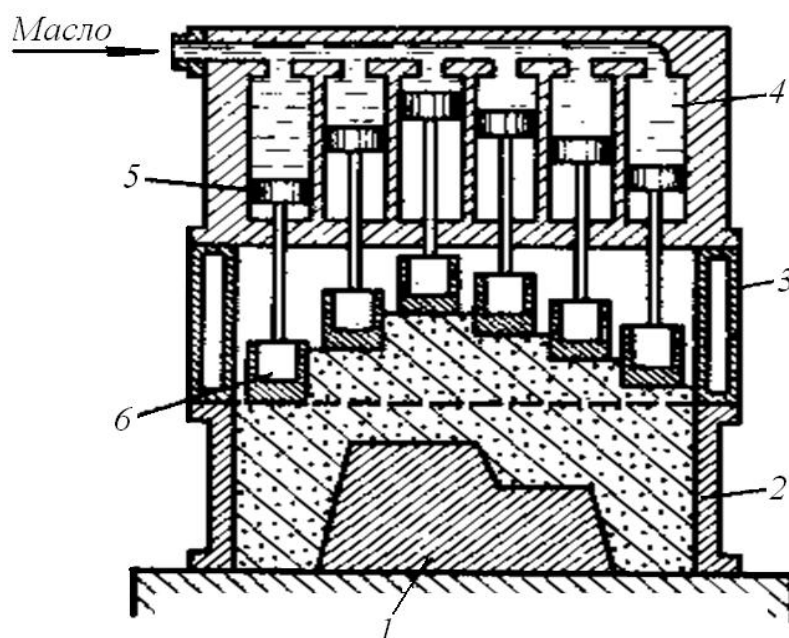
Схема прессования формовочной смеси в опоке многоплунжерной головкой:
